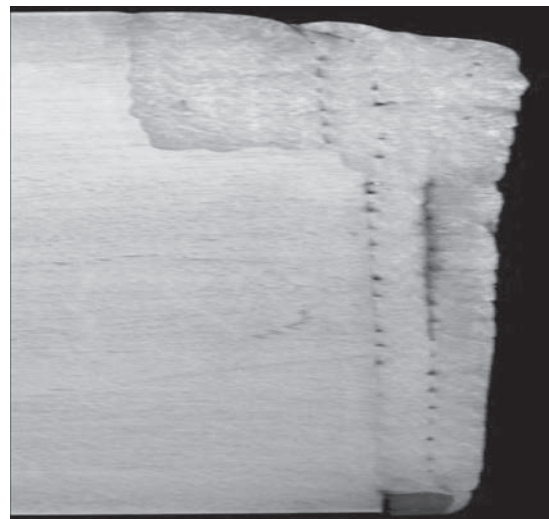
Межслойные (4011) и межваликовые (4012) несплавления при наплавке методом МАГ неповоротной внутренней поверхности трубы диаметром 170 мм
